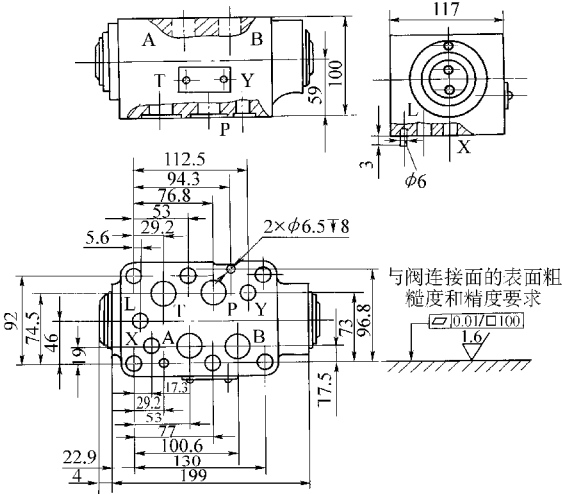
Z2S-22 型叠加式液控单向阀的外形尺寸
